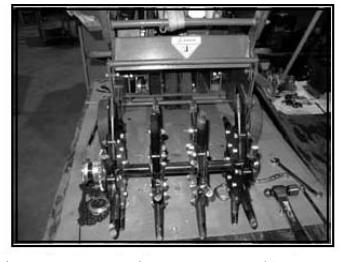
Supprimez complètement le rotor et le mettez de côté avec la chaîne d'enraînement et d'autres composants pour réinstallation
